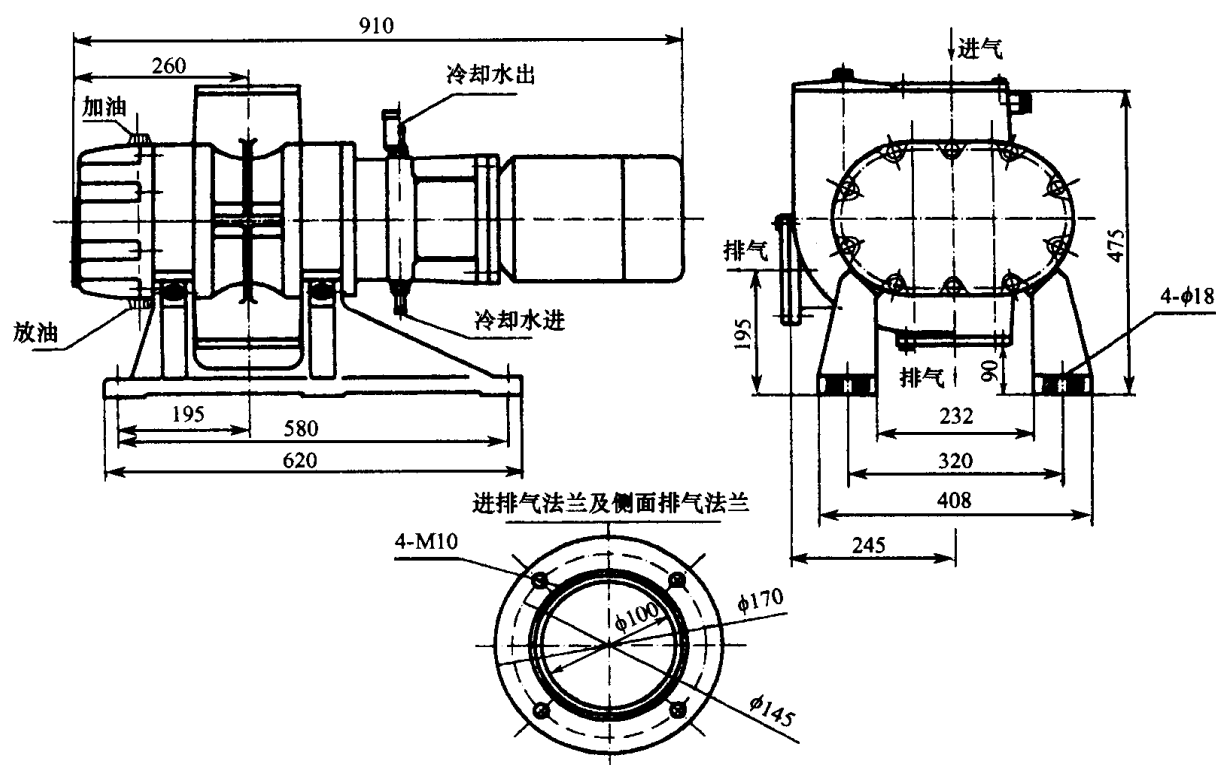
ZJP-70、ZJP-150 型罗茨泵外形及安装尺寸
